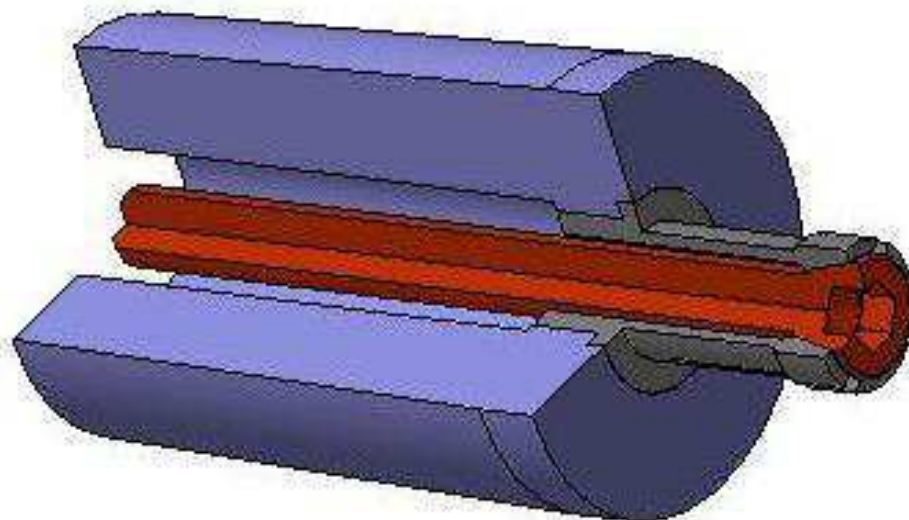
Разрез 3D модели токарного приспособления
